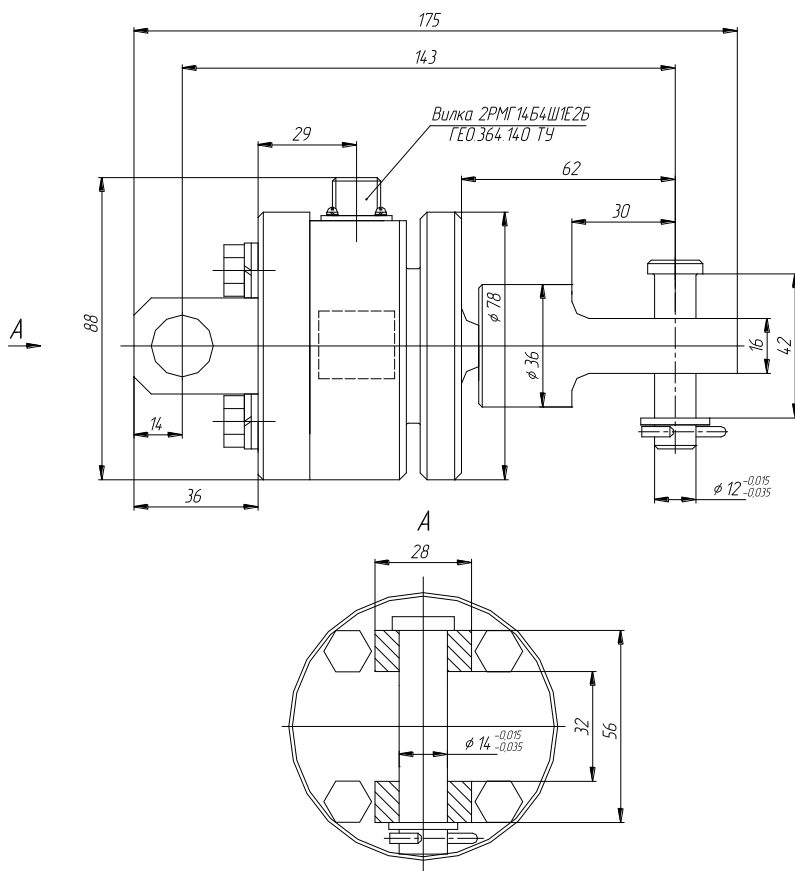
Габаритные и присоединительные размеры датчика усилия
